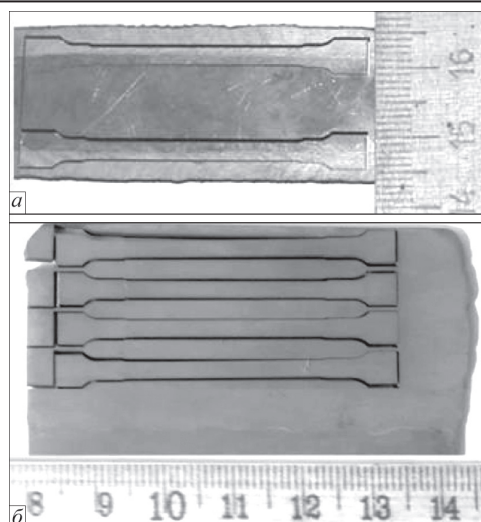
Внешний вид исходных сварных заготовок со схемой вырезки образцов для высокотемпературных механических испытаний: *a* — 50 % ЖС6У(ОМ)+50 % ЖС6К(НМ); *б* — ЖС6К(НМ)
